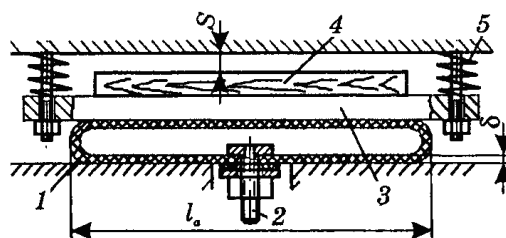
Камерний пневмоциліндр: 1 – камера; 2 – патрубок; 3 – брусок; 4 – заготовка; 5 – пружини
